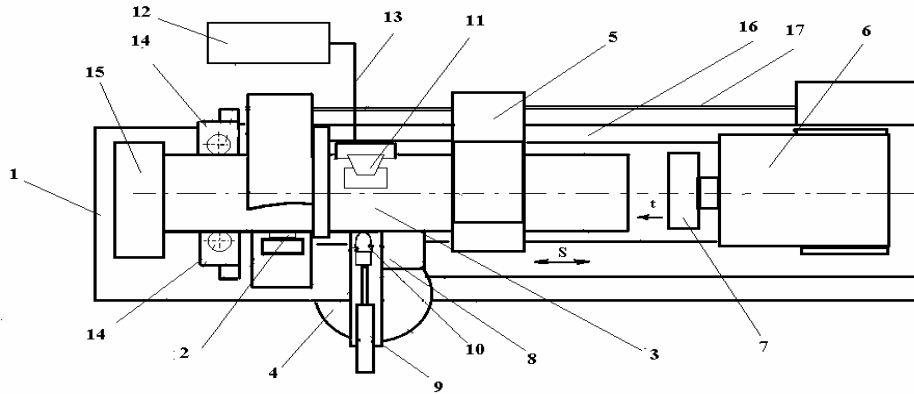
Компоновка универсального станка для токарно-давилных работ
